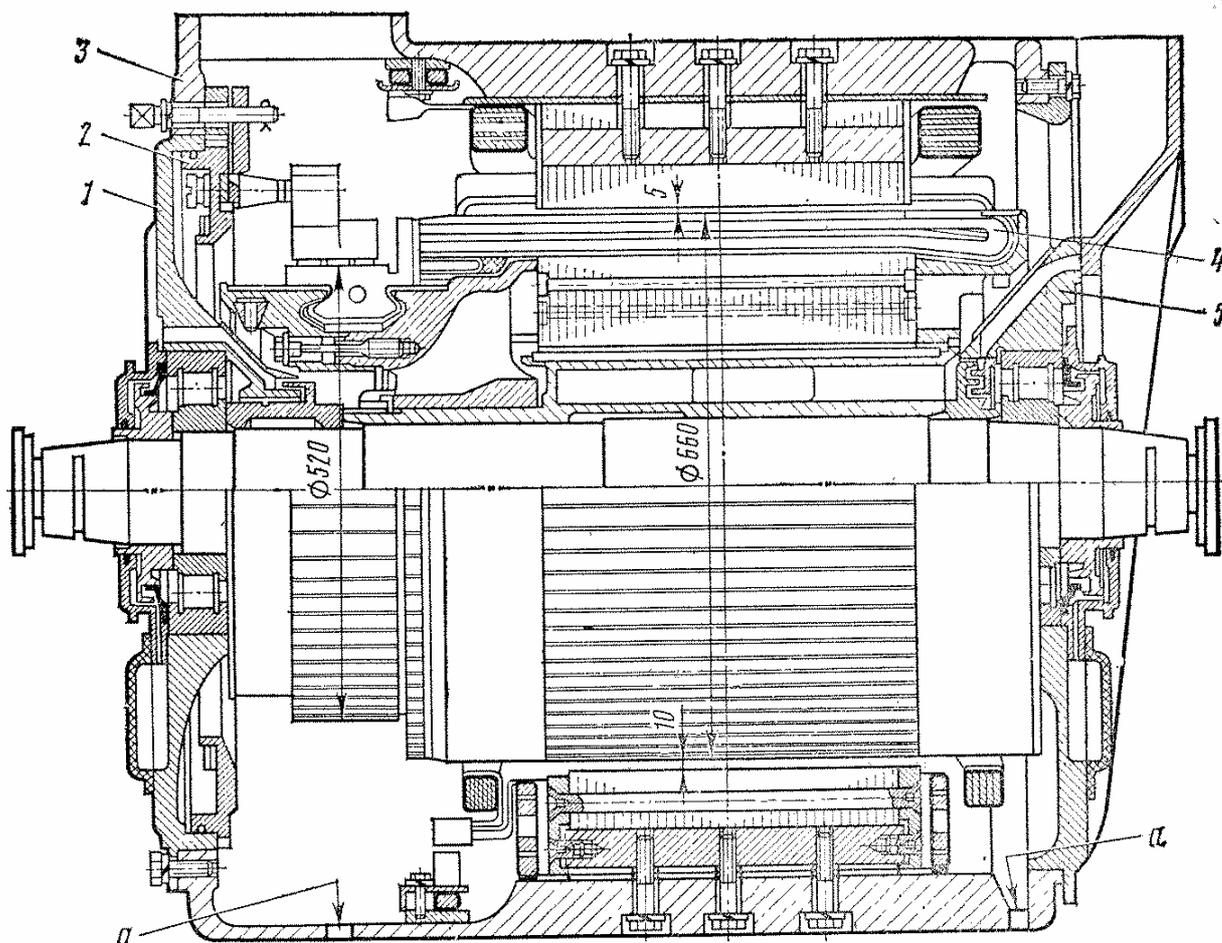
Продольный разрез тягового двигателя НБ-418К6:
